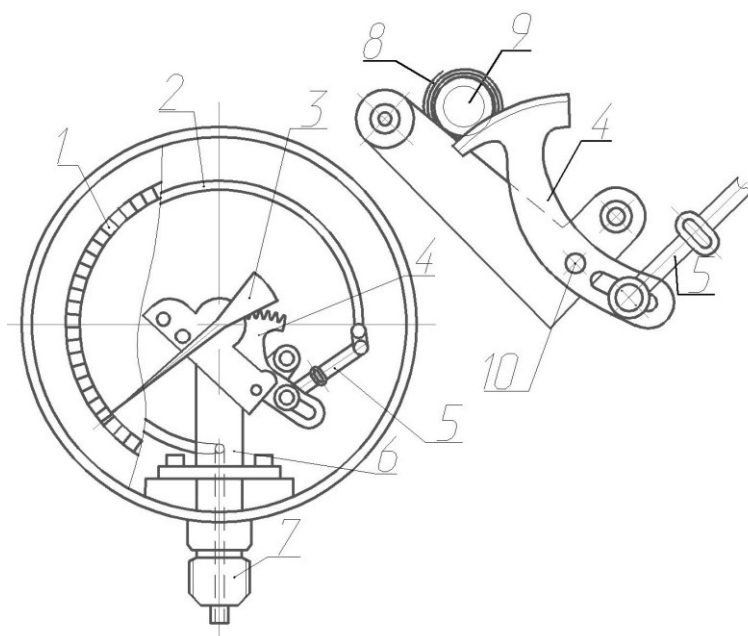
Манометр: 1 – шкала; 2 – плоская трубка; 3 – стрелка; 4 – зубчатый сектор; 5 – регулировочный рычаг; 6 – опора; 7 – штуцер.
